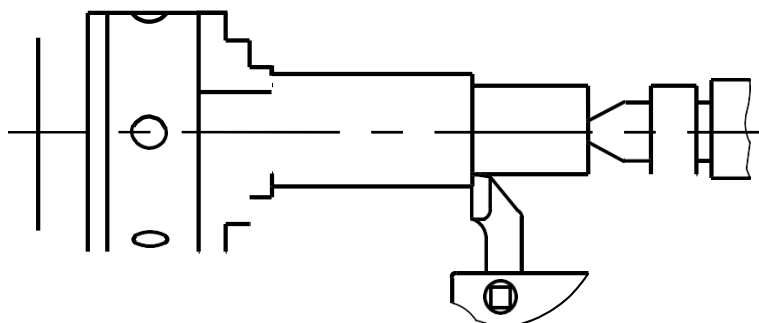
Схема обработки вала с закреплением в патроне и центрированием вращающимся центром задней бабки
